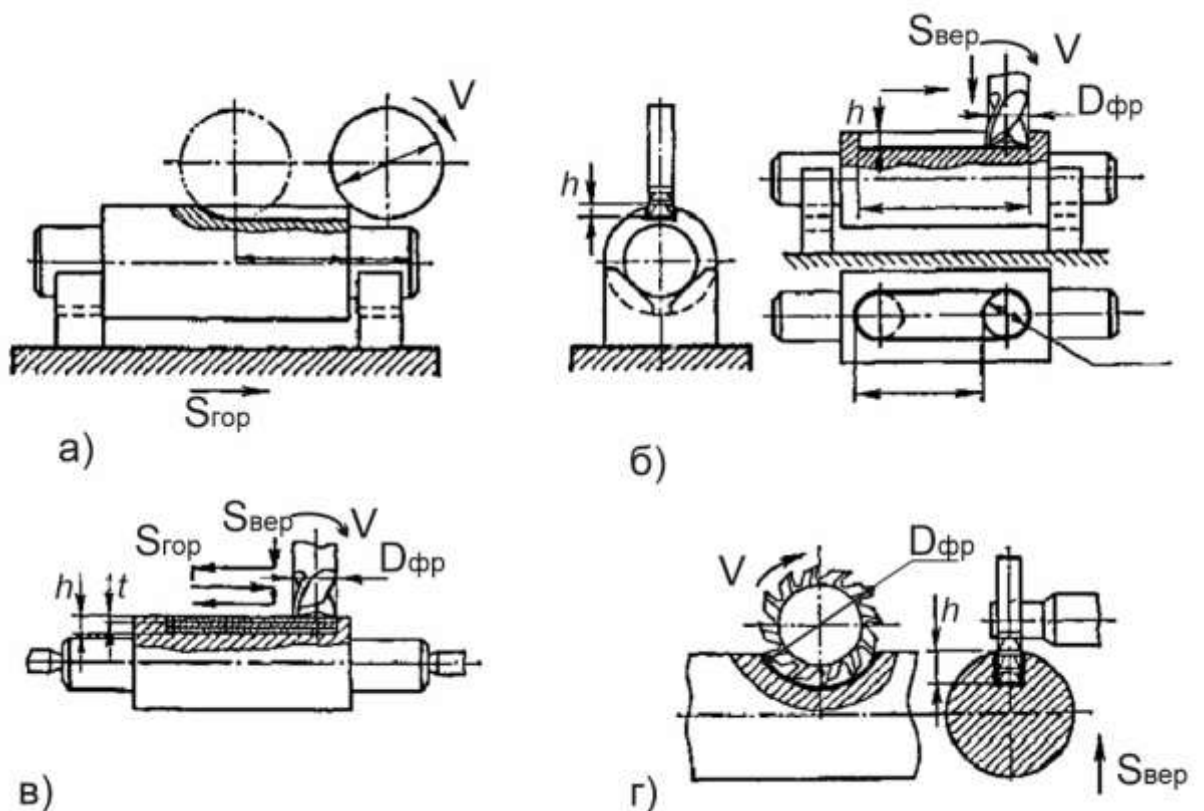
67. Схеми фрезерування шпонкових пазів.
